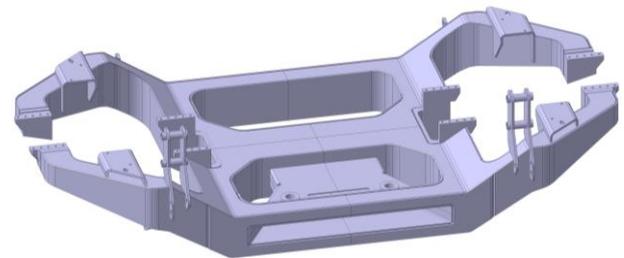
Radträgerschweißbaugruppe
